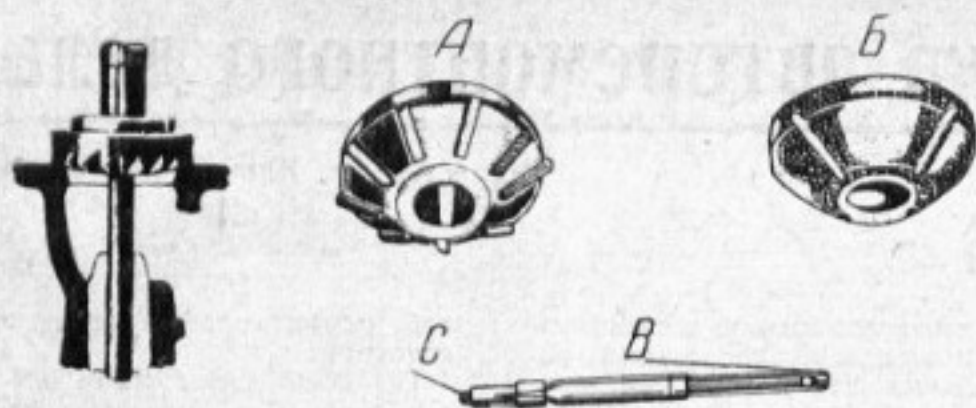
Фреза и шлифовальный камень для ремонта клапанных гнезд
